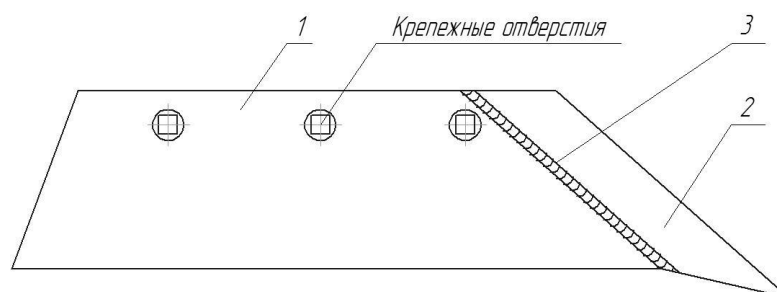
Лемех плуга для отвальной вспашки: 1 – корпус лемеха; 2 – долото (носковая часть); 3 – сварной шов
